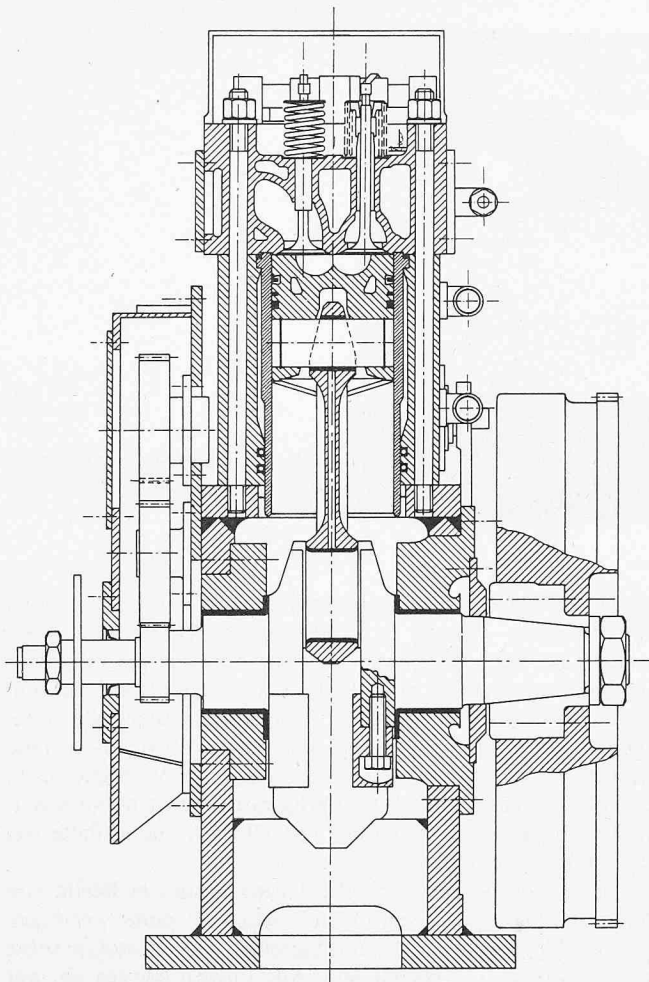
Ansicht des Motors mit Zylinderkopf, Kraftstoffpumpe und Einspritzdüse
